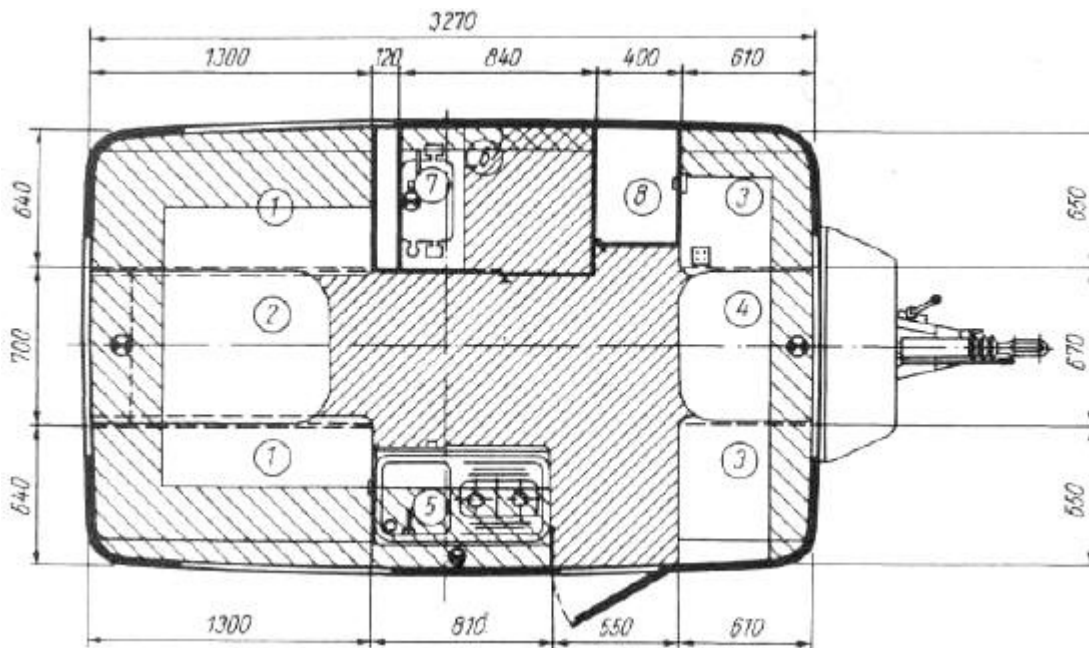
Grundriss eines Campinganhängers mit 3270 mm Aufbau­länge und Liege­flächen für 3 Personen
